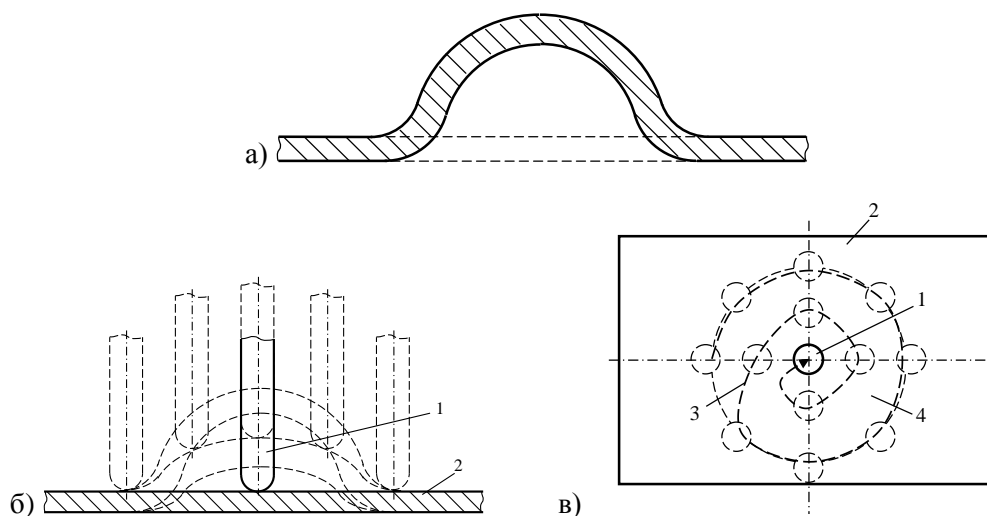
Принципова схема процесу відновлення початкової форми листової заготовки поетапним пластичним деформуванням
